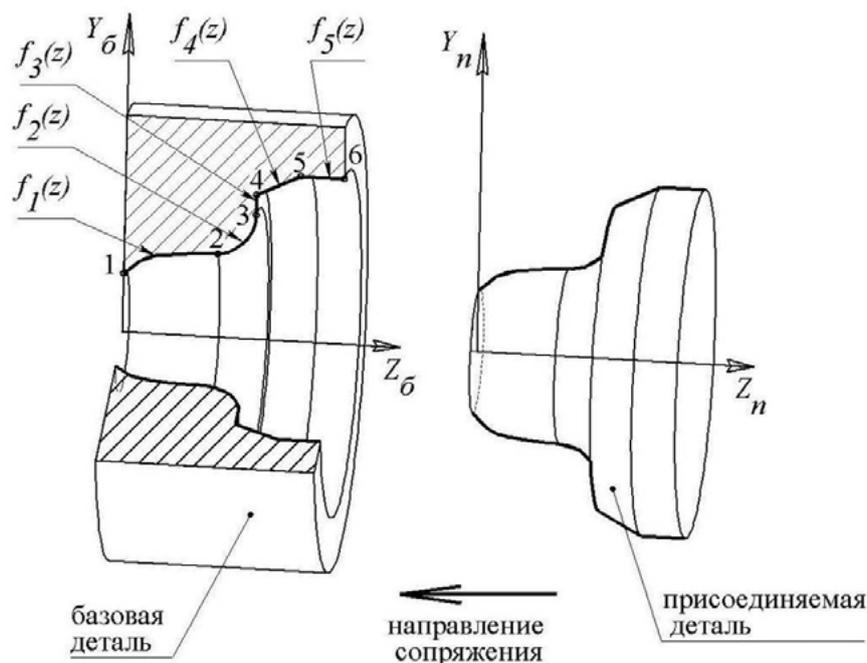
Пример формы образующей сопрягаемой поверхности обрабатываемой на станке базовой детали, которая обеспечивает возможность сопряжения по ней присоединяемой детали вдоль оси симметрии на том же станке без переустановки базовой детали
